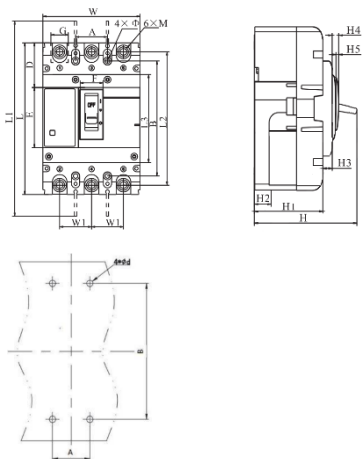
Габаритные и установочные размеры выключателя ВА88
